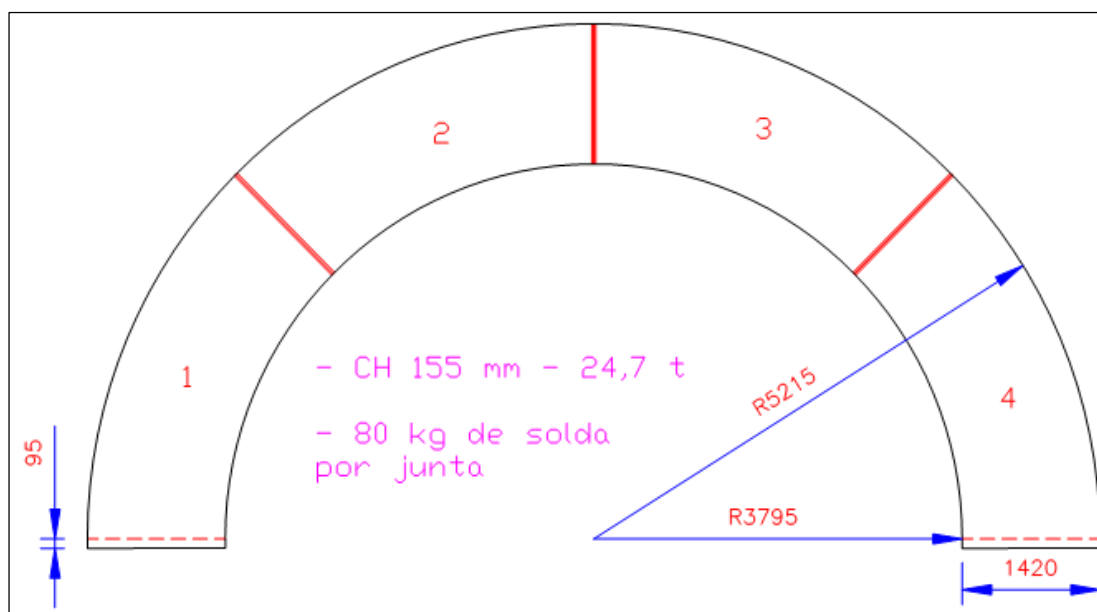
Representação esquemática do anel segmentado soldado pelo Grupo DELP.
